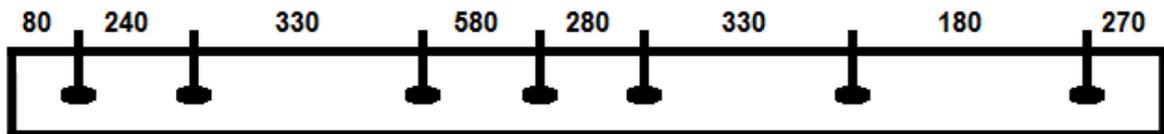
Perfil “U” superior – Lado interno – Vista frontal - fixação do trilho no perfil “U”
